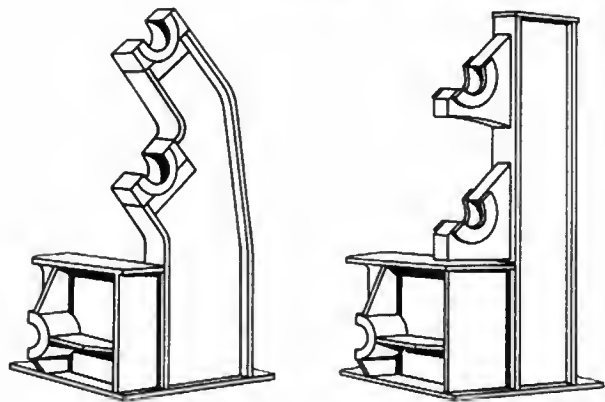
Deux solutions soudées pour un bâti
